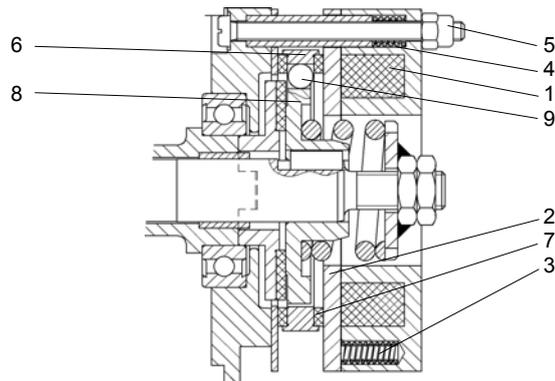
Aufbau der Bremse für Bauformen 2-9.1
